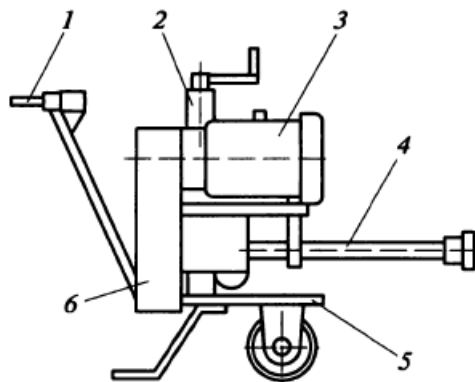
Схема гайковерта для крепления колес: 1 — пульт управления; 2 — механизм подъема и опускания; 3 — электродвигатель; 4 — выходной вал; 5 — основание; 6 — приводной механизм
